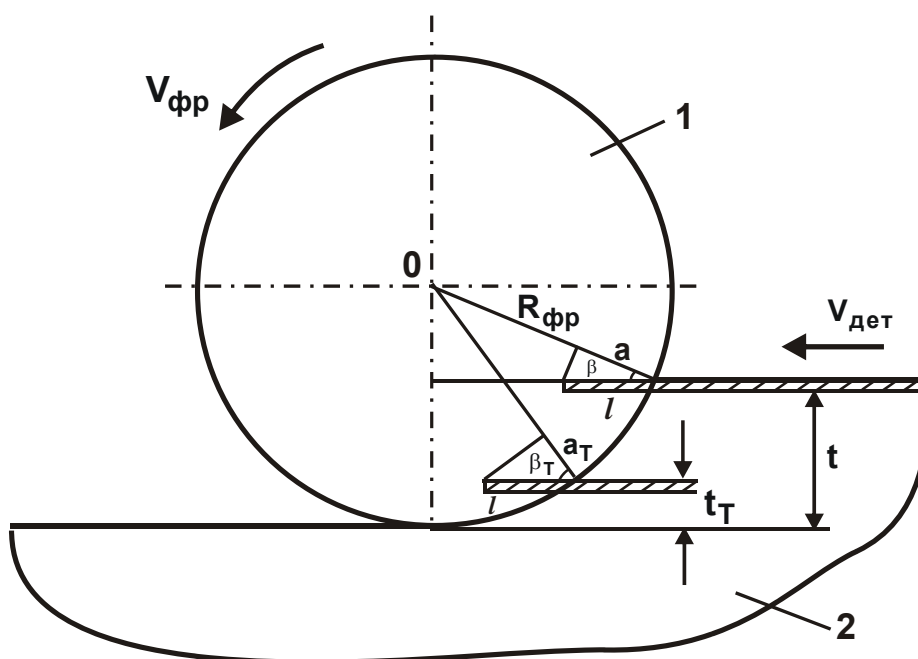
Расчетная схема параметров фрезерования цилиндрической фрезой: 1 – контур фрезы; 2 – обрабатываемая деталь
